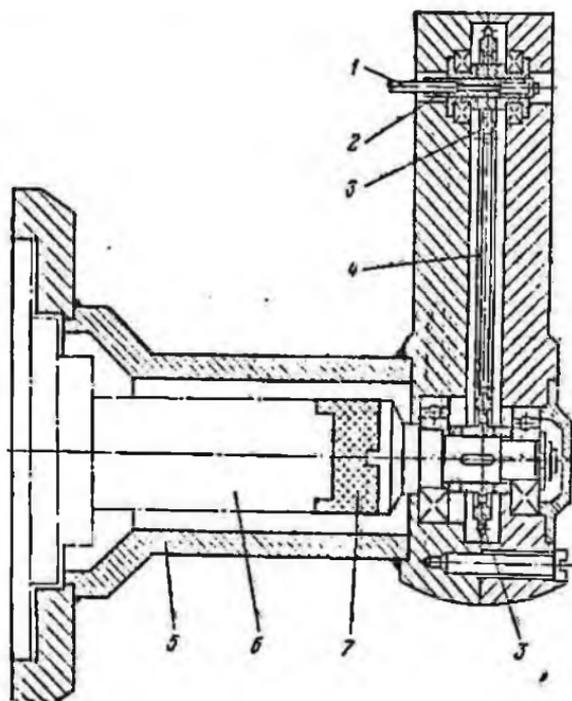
Приспособление для фрезеровки внутренних шлицевых пазов:
